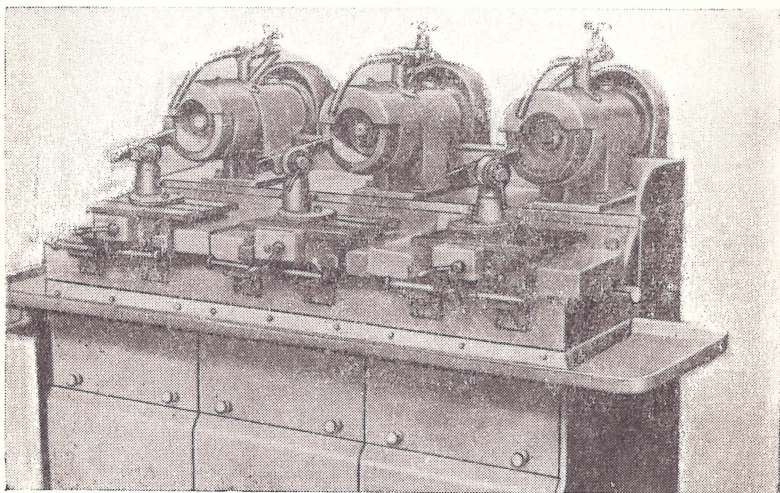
Трехшпиндельный полуавтоматический заточной станок
